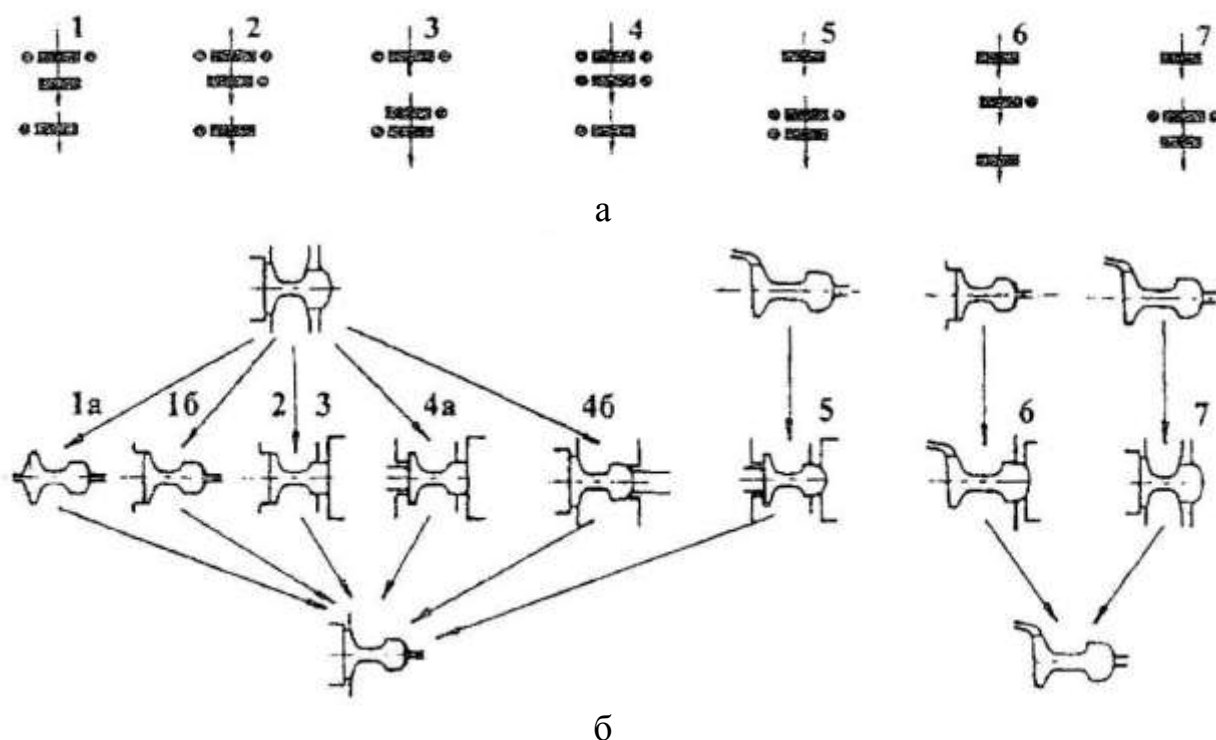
Типовая схема калибровки для прокатки рельсов фирмы SMS [3]
